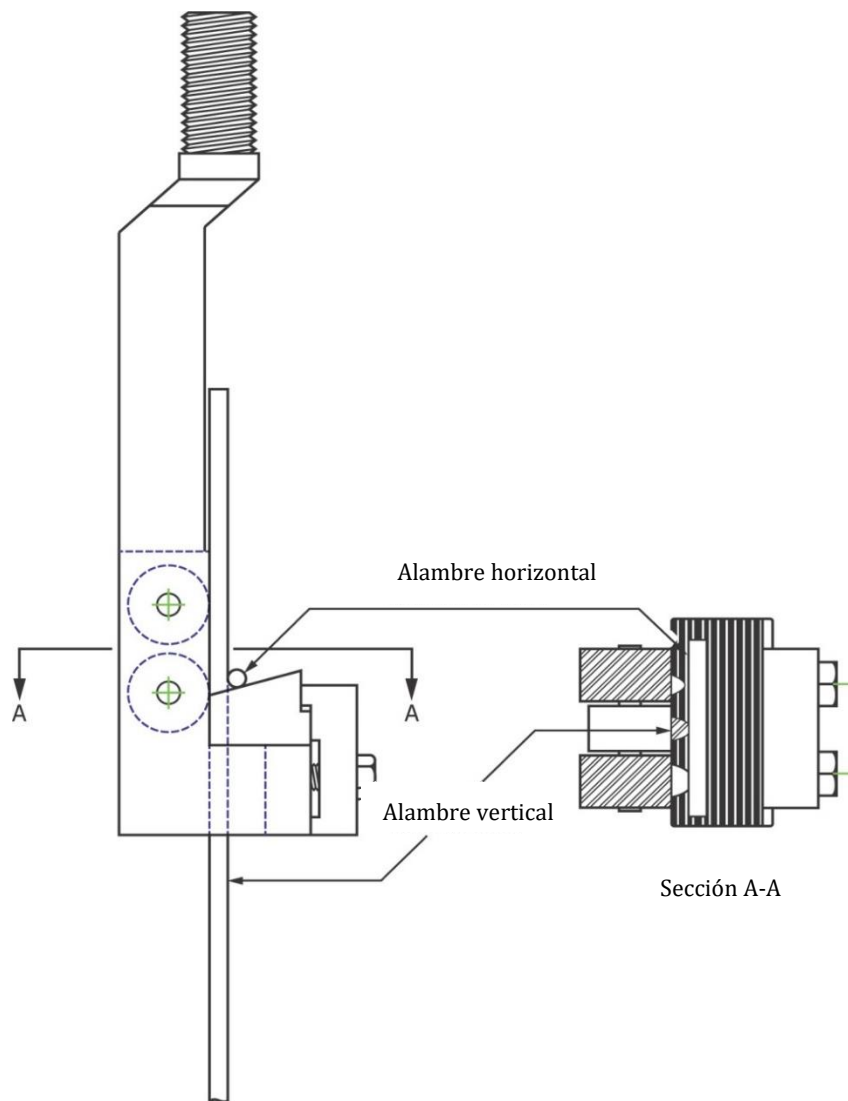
Probador de Soldadura para Refuerzo de Alambre Soldado
